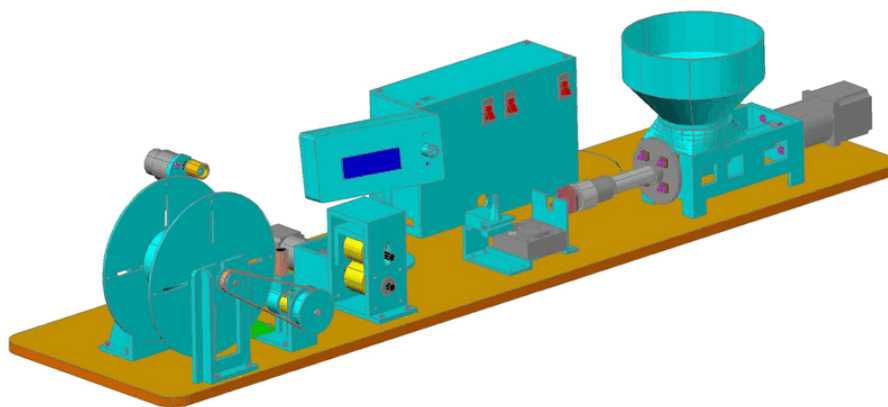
Устройство в сборе для изготовления пластиковой нити для печати на 3D принтере (FDM)
